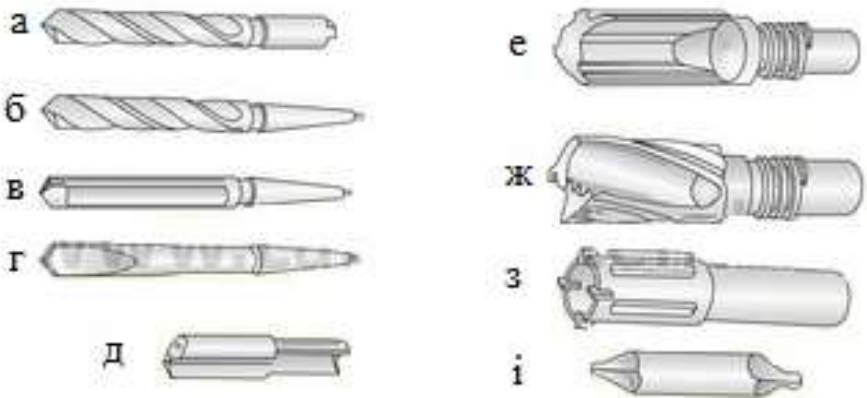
Свердла: а, б – спіральні; в – з прямими канавками; г – перове; д – спеціальне; е – однокромочне з внутрішнім відводом стружки для глибокого свердління; ж – двокромочне для глибокого свердління; з – для кільцевого свердління; і – центрувальне
